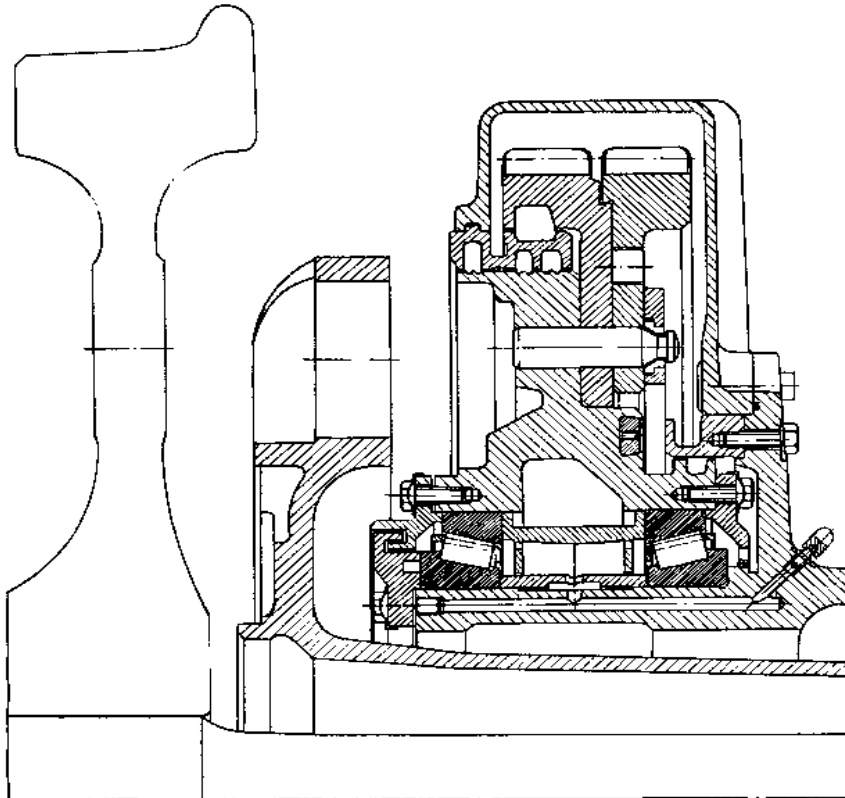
大齿轮支架装配两套锥形滚柱轴承或两套角面接触的滚珠轴承
